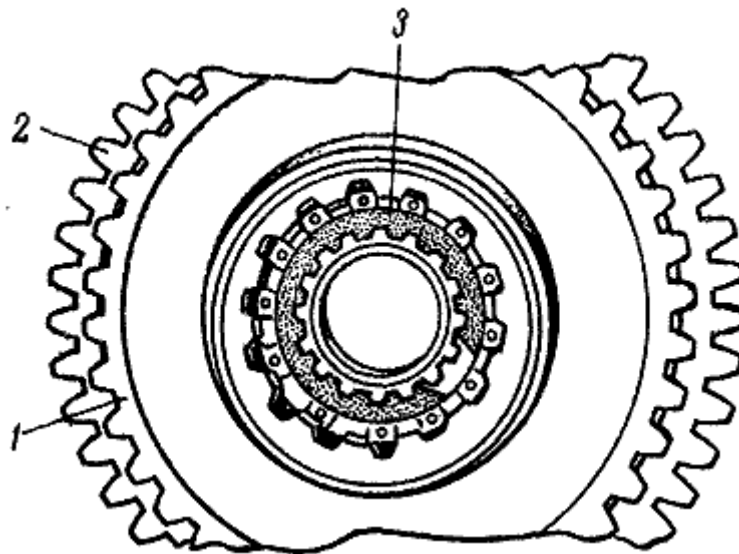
Снятие стопорного кольца шестерен I и II ступеней привода
